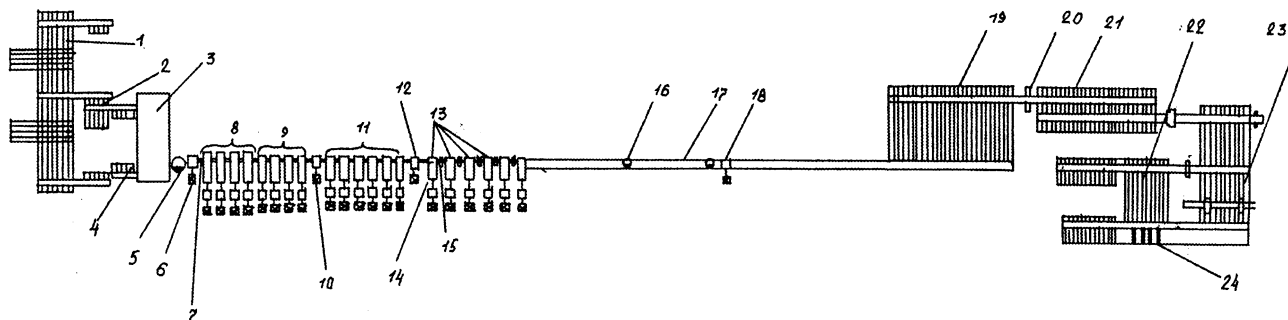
Схема расположения основного технологического оборудования стана 320 РУП «БМЗ»: 1 – загрузочная решетка; 2 – устройство для загрузки заготовок; 3 – нагревательная печь; 4 – устройство выдачи заготовок (разгрузочный рольганг); 5 – трайб-аппарат; 6 – маятниковые ножницы; 7 – устройство для удаления окалины; 8, 9 – черновая группа клеток; 10, 12, 18 – ротационные ножницы; 11 – промежуточная группа клеток; 13 – горизонтальные клетки чистовой группы; 14 – вертикальные клетки чистовой группы; 15 – комбинированные петлерегуляторы; 16 – трайб-аппараты; 17 – устройство для охлаждения проката с рольгангом; 19 – холодильник; 20 – правильная машина; 21 – цепное переключательное устройство с накопителем; 22 – участок пакетирования фасонного проката; 23 – участок пакетирования пруткового проката; 24 – вязальные машины
